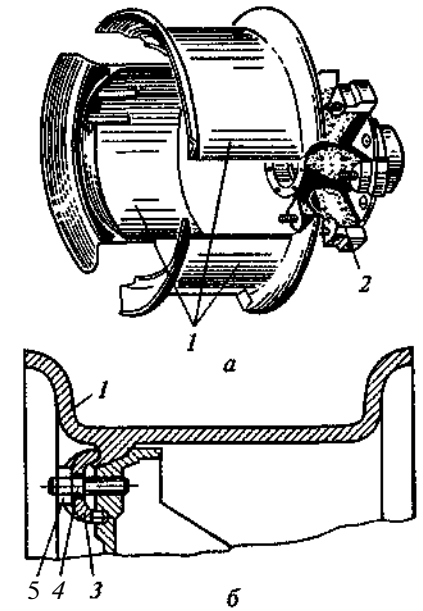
Конструкция (а) и крепление (б) бездискового колеса: 1 — секторы; 2 — ступица; 3 — прижим; 4 — шпилька; 5 — гайка
